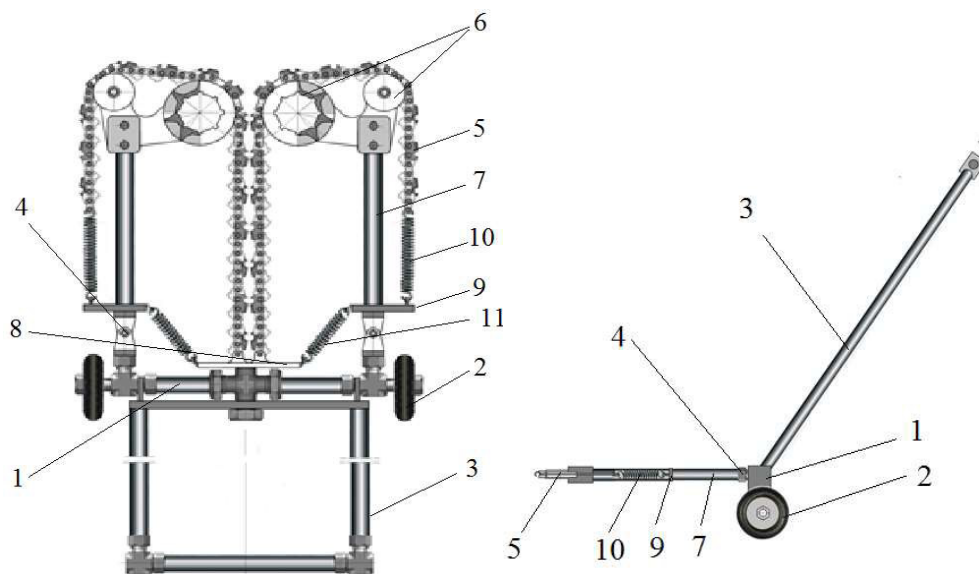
Передвижное устройство для кольцевания деревьев: 1 – рама, 2 – ходовые колёса, 3 – направляющая П-образной формы, 4 – шарниры, 5 – пильные цепи, 6 – звёздочки, 7 – стяжки, 8 – центральная планка, 9 – боковые планки, 10, 11 – пружины
